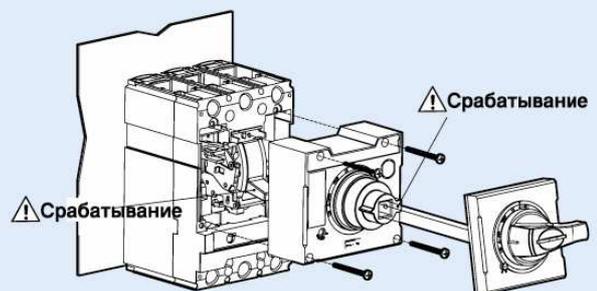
Габаритные и установочные размеры, способ установки выносных поворотных рукояток TD100 - TD160
